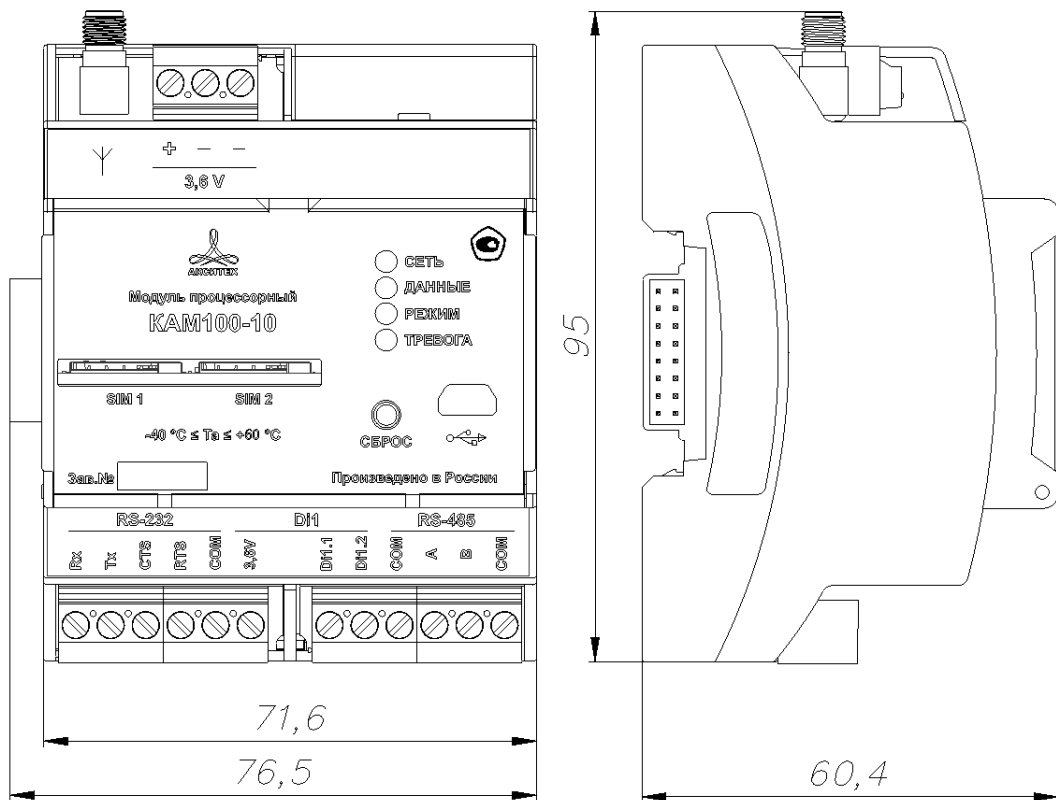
Внешний вид и габаритные размеры модуля процессорного КАМ100-10
